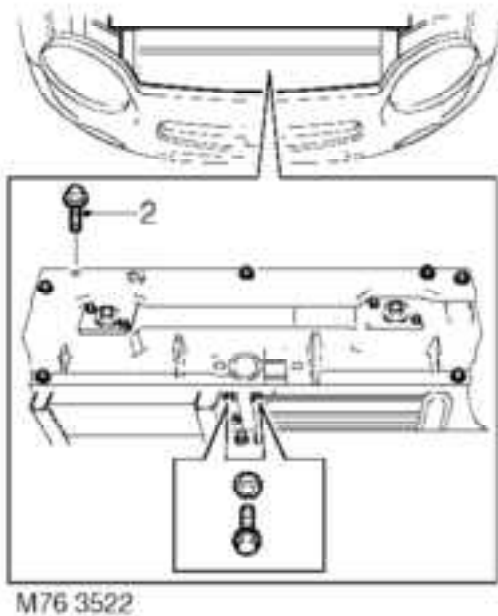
PLATE-FORME DE VERROU DE CAPOT - DEPOSE ET REPOSE POUR ACCES
